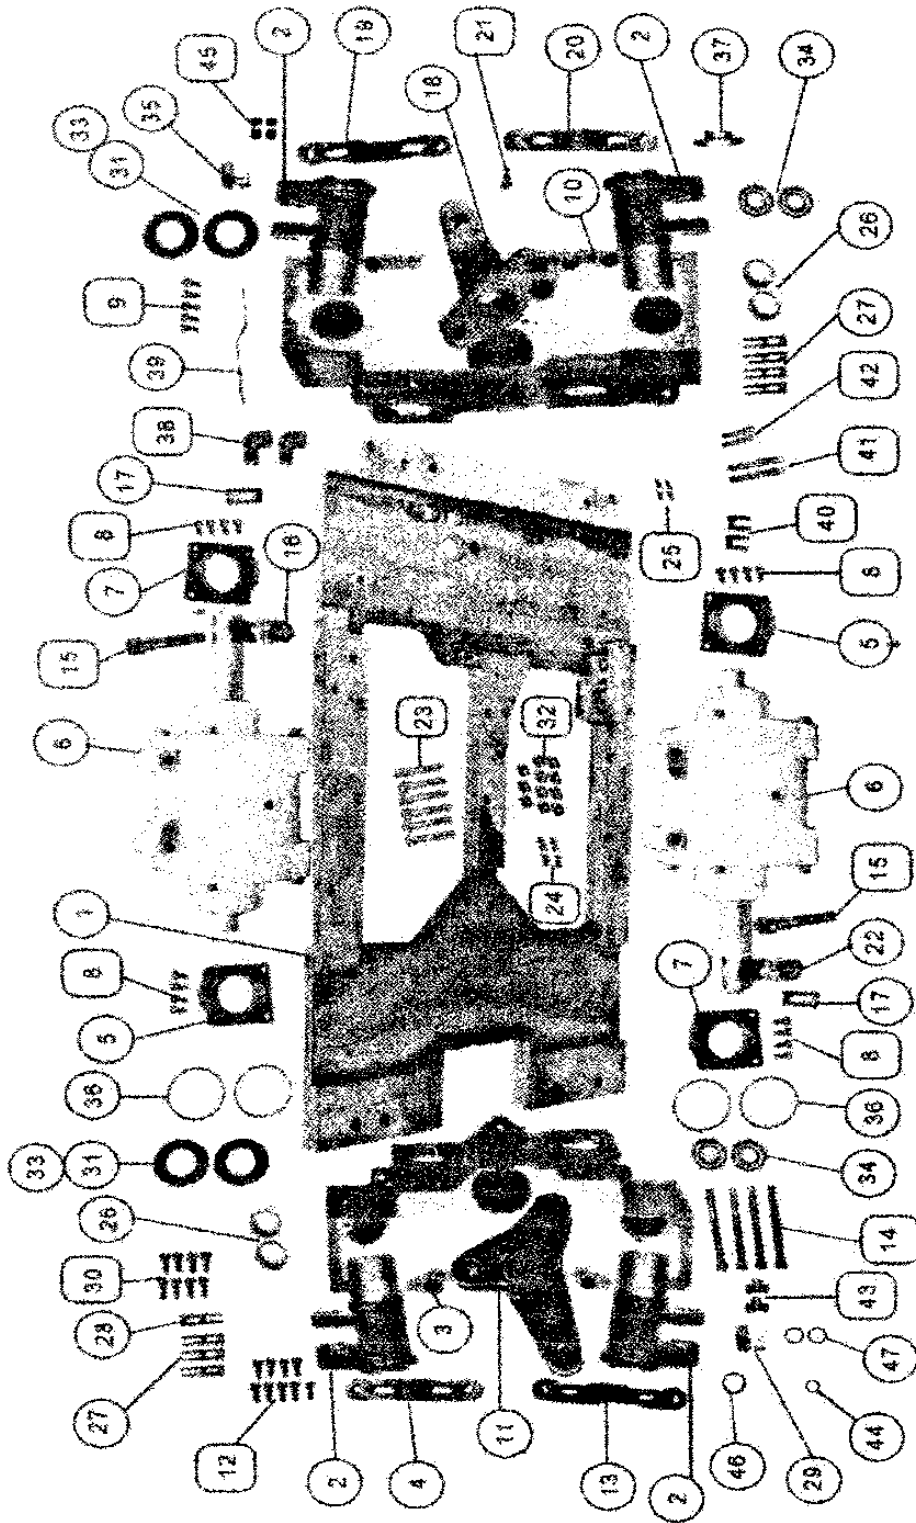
Partes Desmontadas del Mecanismo de Abrir y Cerrar Molde.
